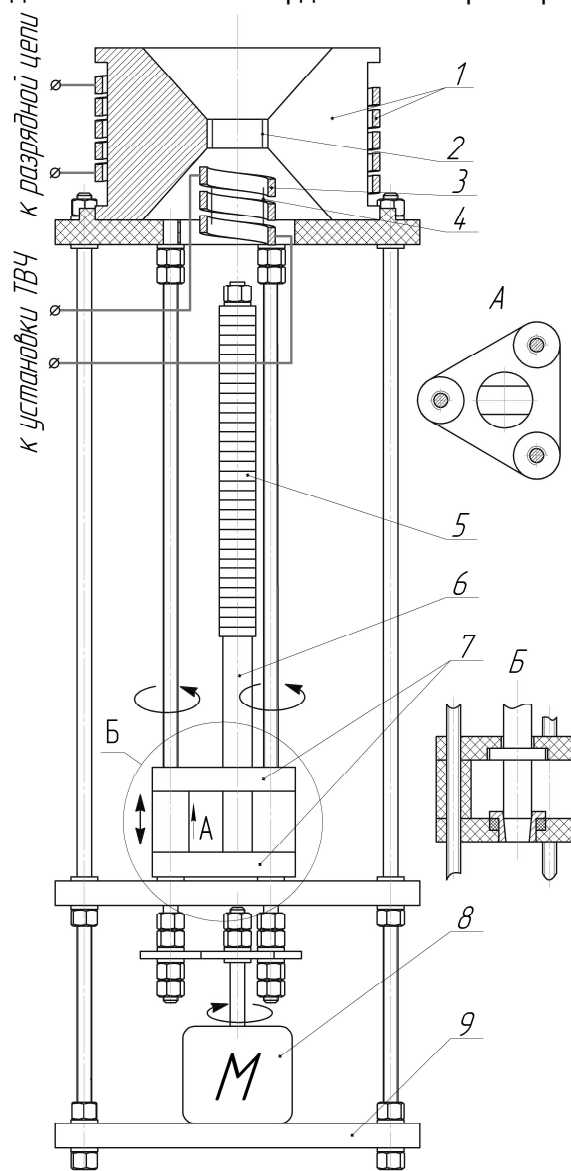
Схема модернизированного устройства для КМИО: 1– индуктор импульсного магнитного поля; 2 – зона обработки импульсным магнитным полем; 3– индуктор установки ТВЧ; 4– зона предварительного нагрева изделия ТВЧ; 5– обрабатываемые изделия; 6– шпилька; 7– механизм подачи ; 8– шаговый двигатель; 9– рама.
